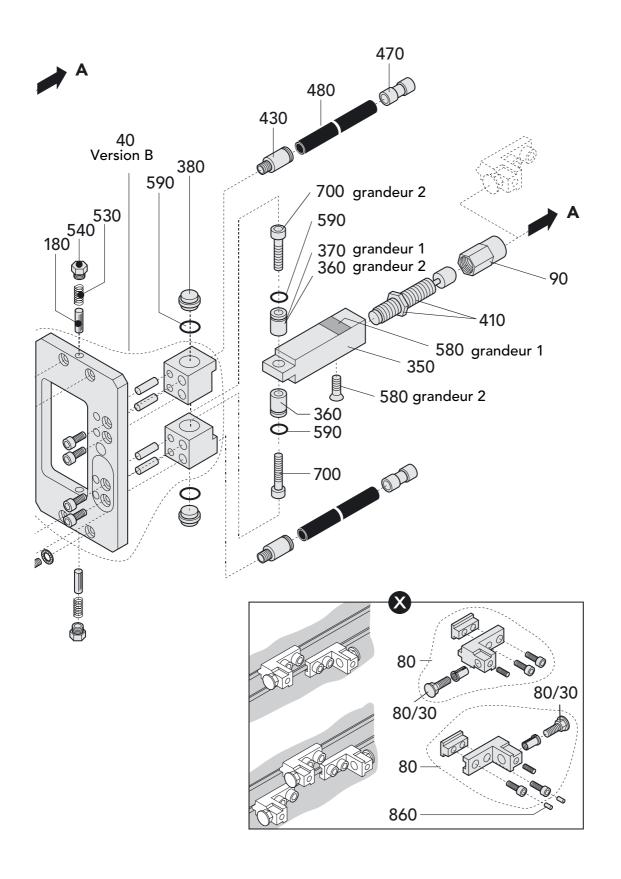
Dessin d'explosion des unités horizontales
